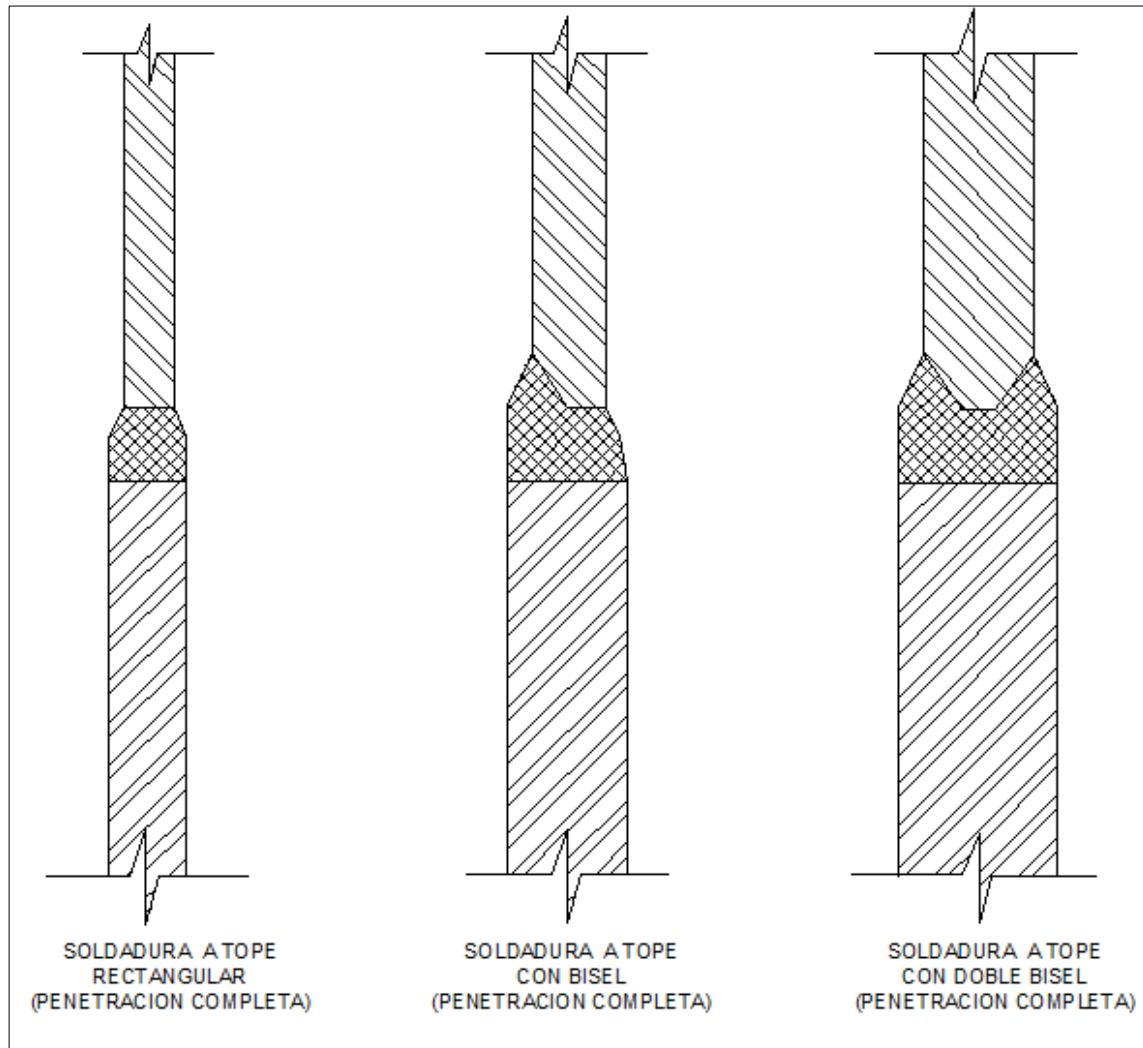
Detalles Típicos de Soldaduras Circunferenciales.
